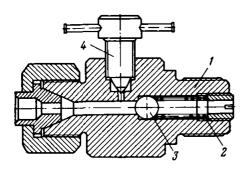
Масляный обратный клапан: 1 -корпус; 2 -пружина; 3 -шарик; 4 -контрольный краник
